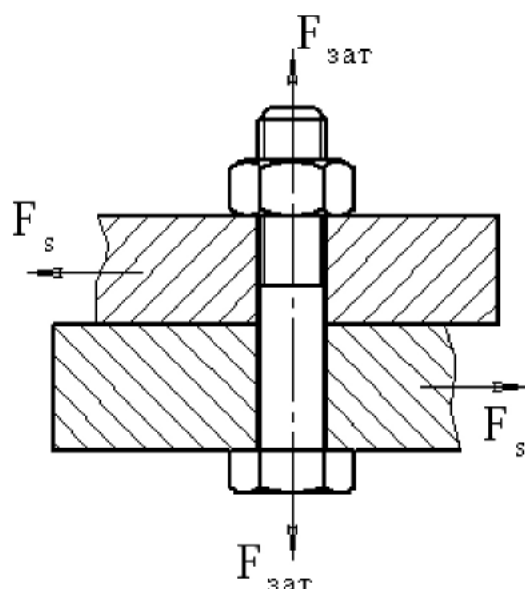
Схема резьбового соединения, нагруженного сдвигающей нагрузкой
